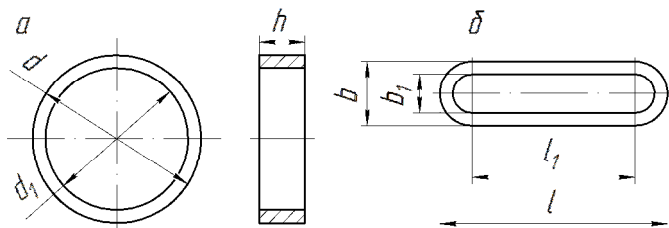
Розміри заготовки і пружної шпонки з порожниною еквидистантною зовнішньому обрису
